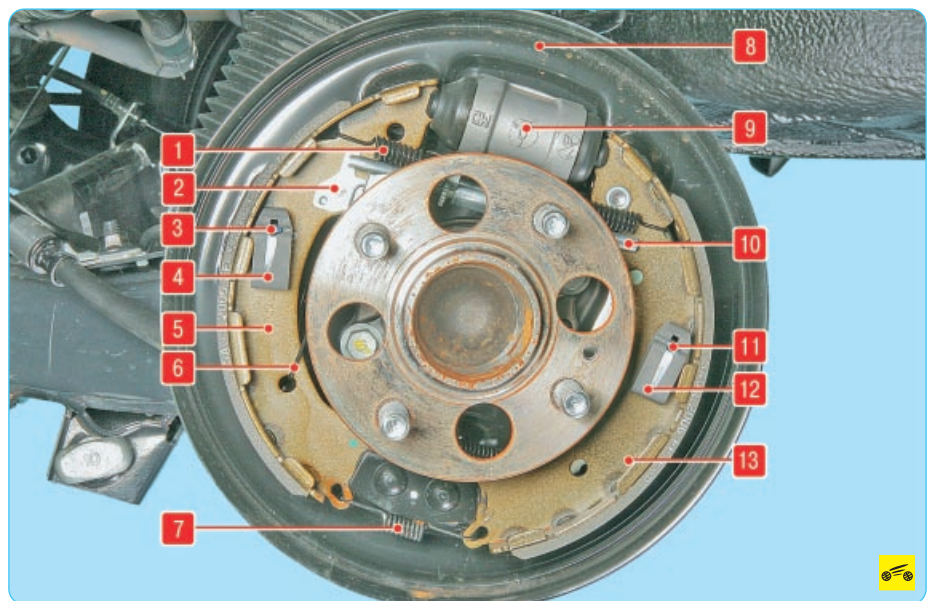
Барабанный тормозной механизм заднего колеса (для наглядности тормозной барабан снят): 1 – верхняя стяжная пружина; 2 – рычаг регулятора зазора; 3, 11 – стержни опорных стоек колодок; 4, 12 – пружинные пластины; 5 – передняя тормозная колодка; 6 – пружина рычага регулятора зазора; 7 – нижняя стяжная пружина; 8 – тормозной щит; 9 – рабочий тормозной цилиндр; 10 – распорная планка; 13 – задняя тормозная колодка
